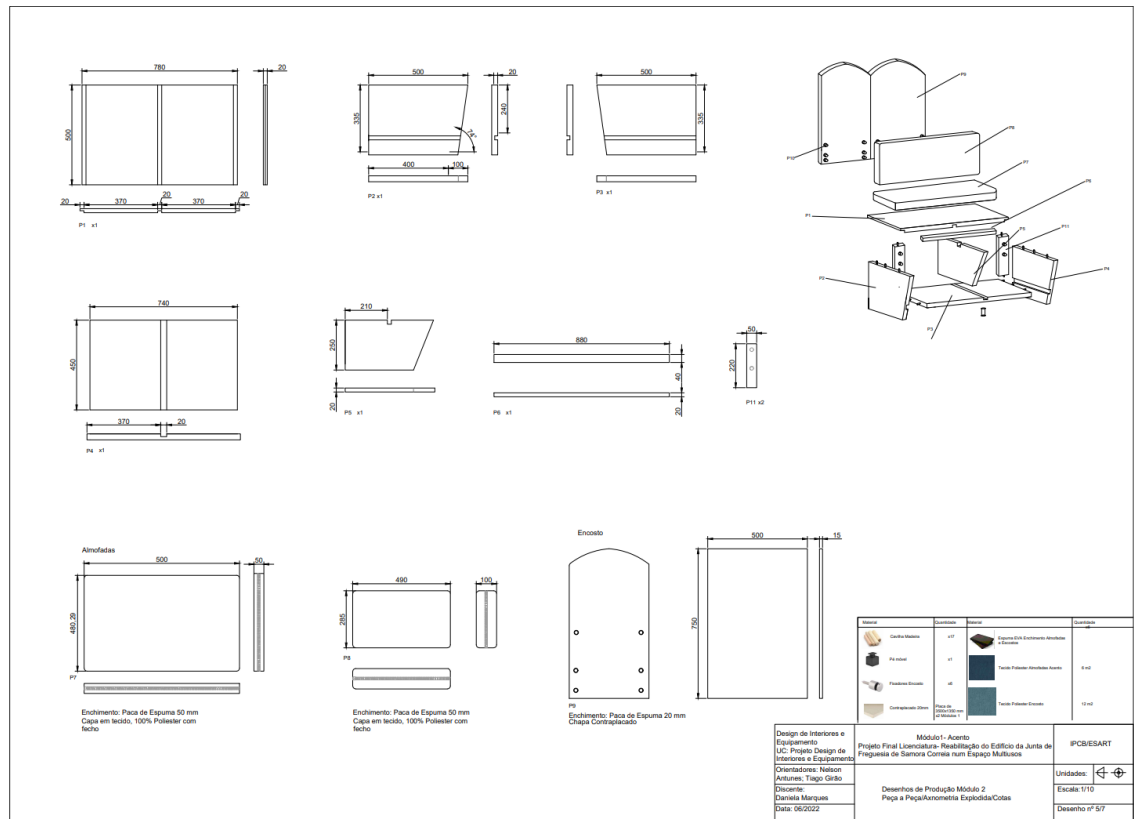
Figura 102-Desenho Técnico Produção Módulo 2
